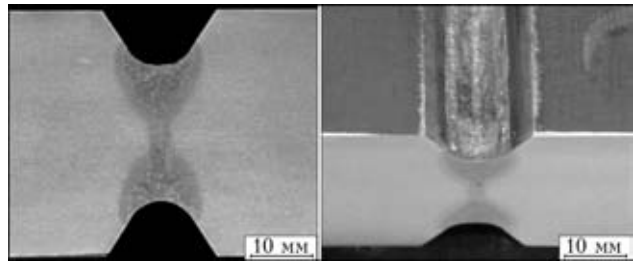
Макрошлиф сварных соединений, полученных на пластинах стали шириной 38 мм двухсторонней однопроходной сваркой с разделкой кромок под углом 70°
